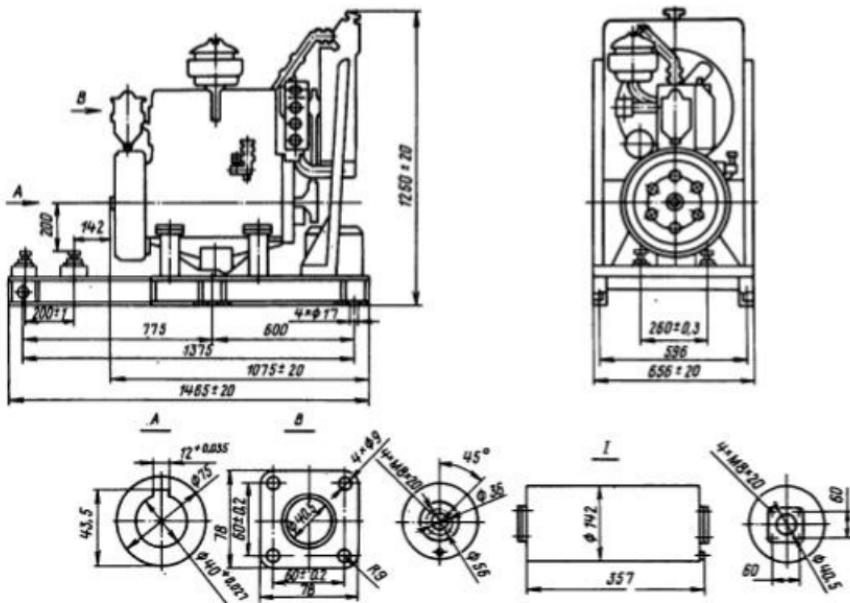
Габаритный чертеж дизеля 4ч 8,5/11 (2Р4-С, 2Р4-С1):
